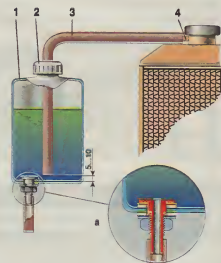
Самодельный бачок из полиэтиленовой банки: 1 — банка; 2 — пробка банки; 3 — шланг; 4 — паровотводная трубка; а — вариант патрубков из металла.
